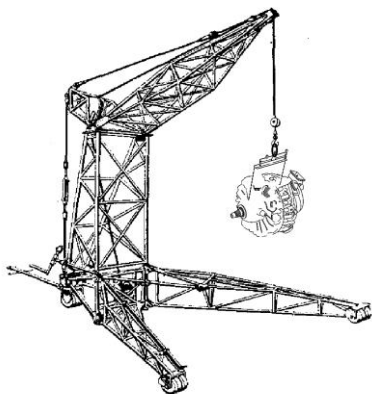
Conjunto de guincho e estrutura (talha) usado para remoção de motor.
